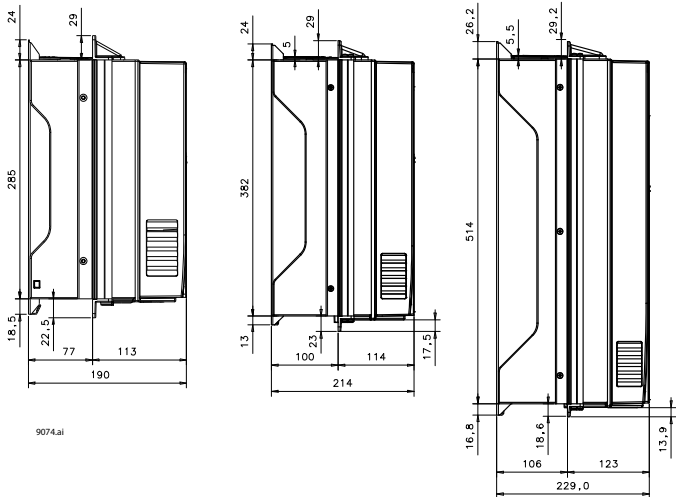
MR4 a MR6, montagem com flange, dimensões de profundidade
